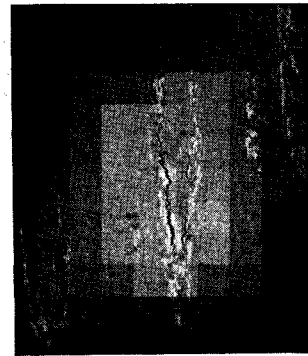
Walzzungen auf einem Blech mit strichförmig angeordneten Pickeln (rd. 10:1)
